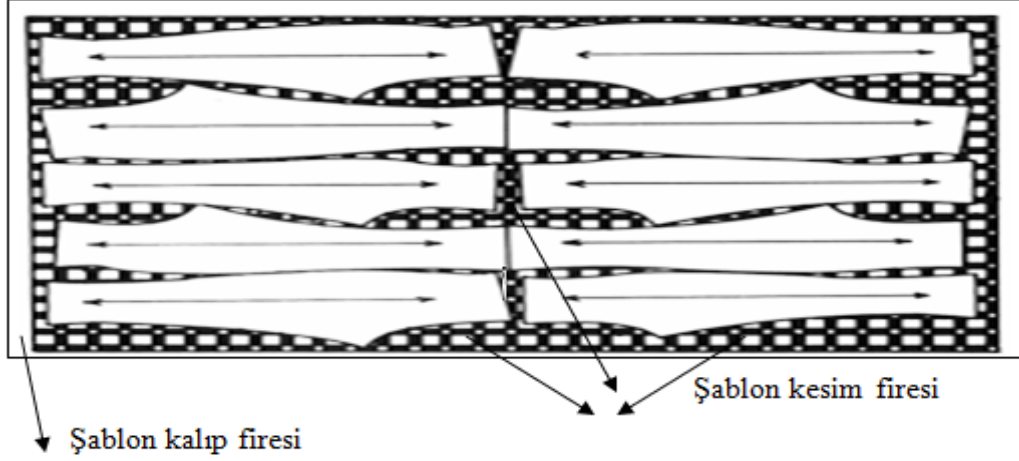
Ceplik Pastal Planı (Rembrandt)
